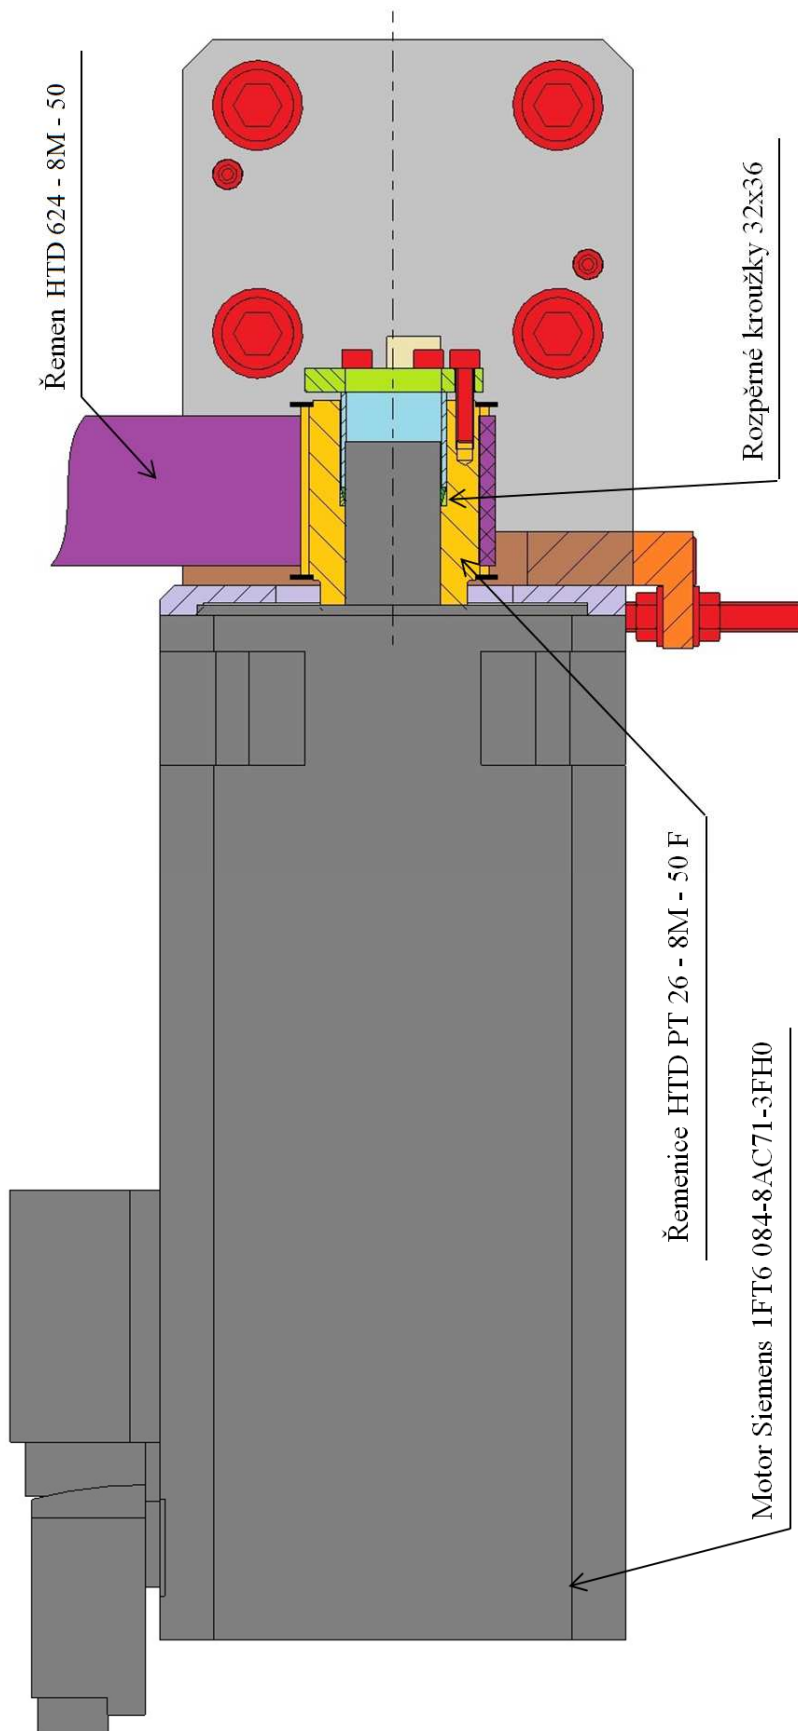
Konstrukční řešení podélného posuvu - ISO pohled
